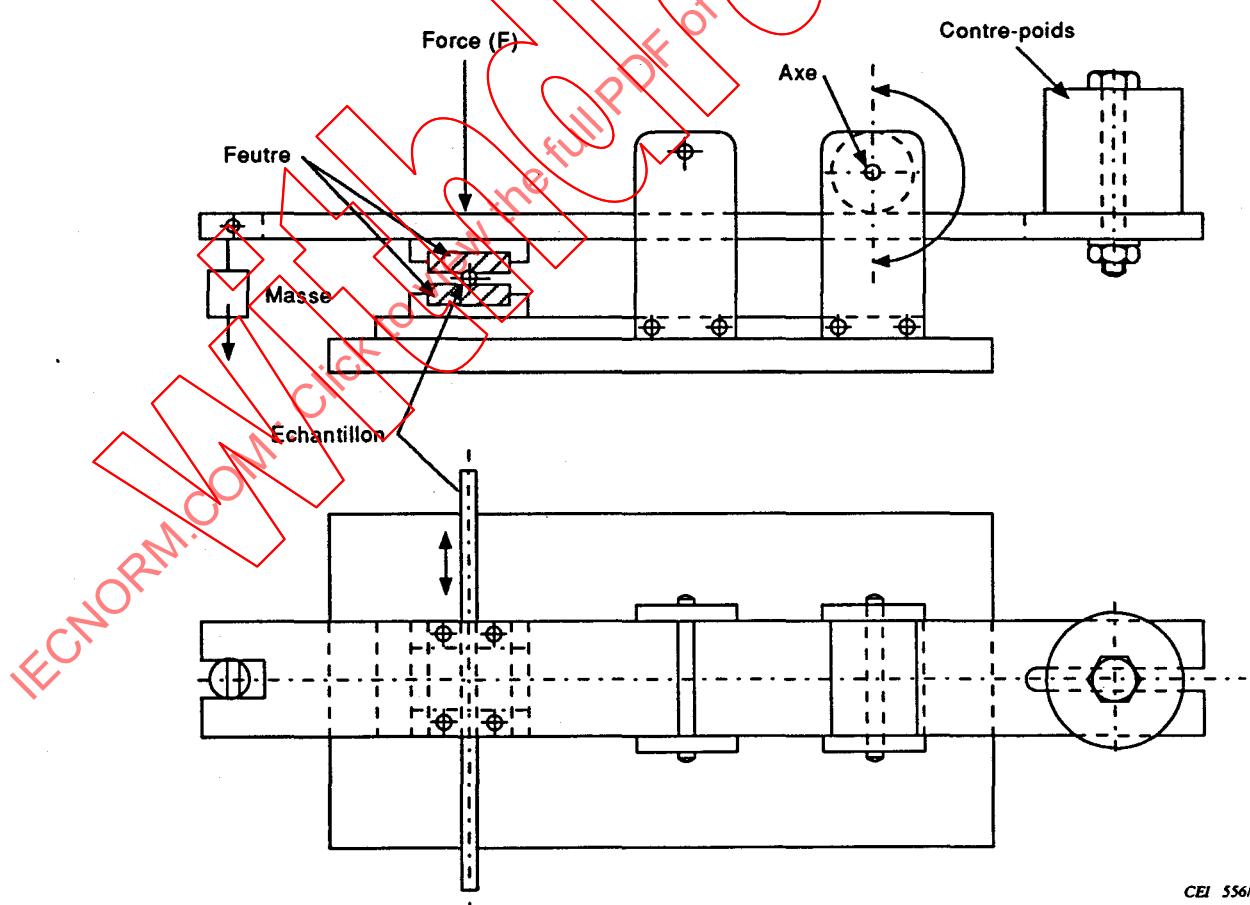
Appareillage d'essai typique pour l'essai E2B, méthode 2
